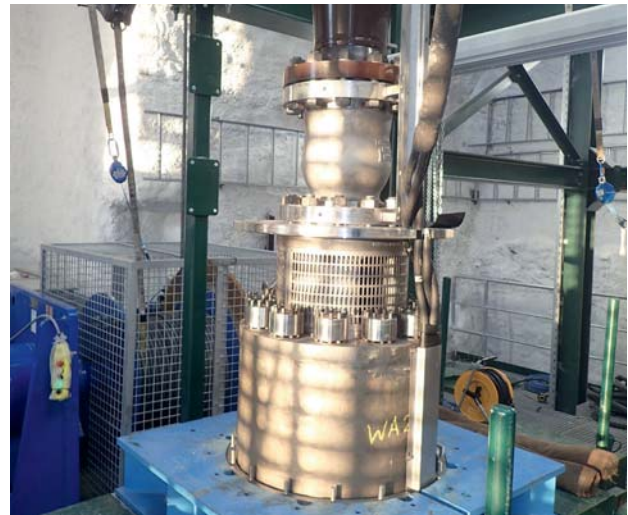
Einbau einer Pumpe mit Kühlmantel
